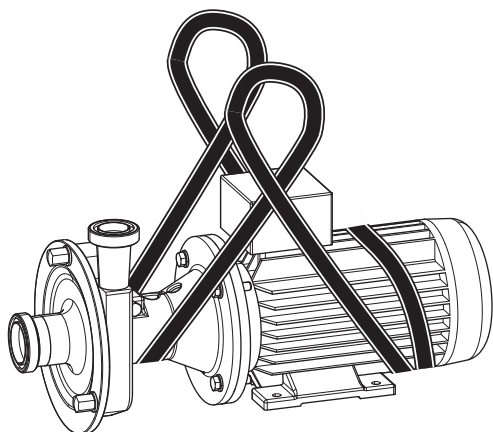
Транспортировка с помощью кольцевого стропа на примере конструктивного типа FSPE
